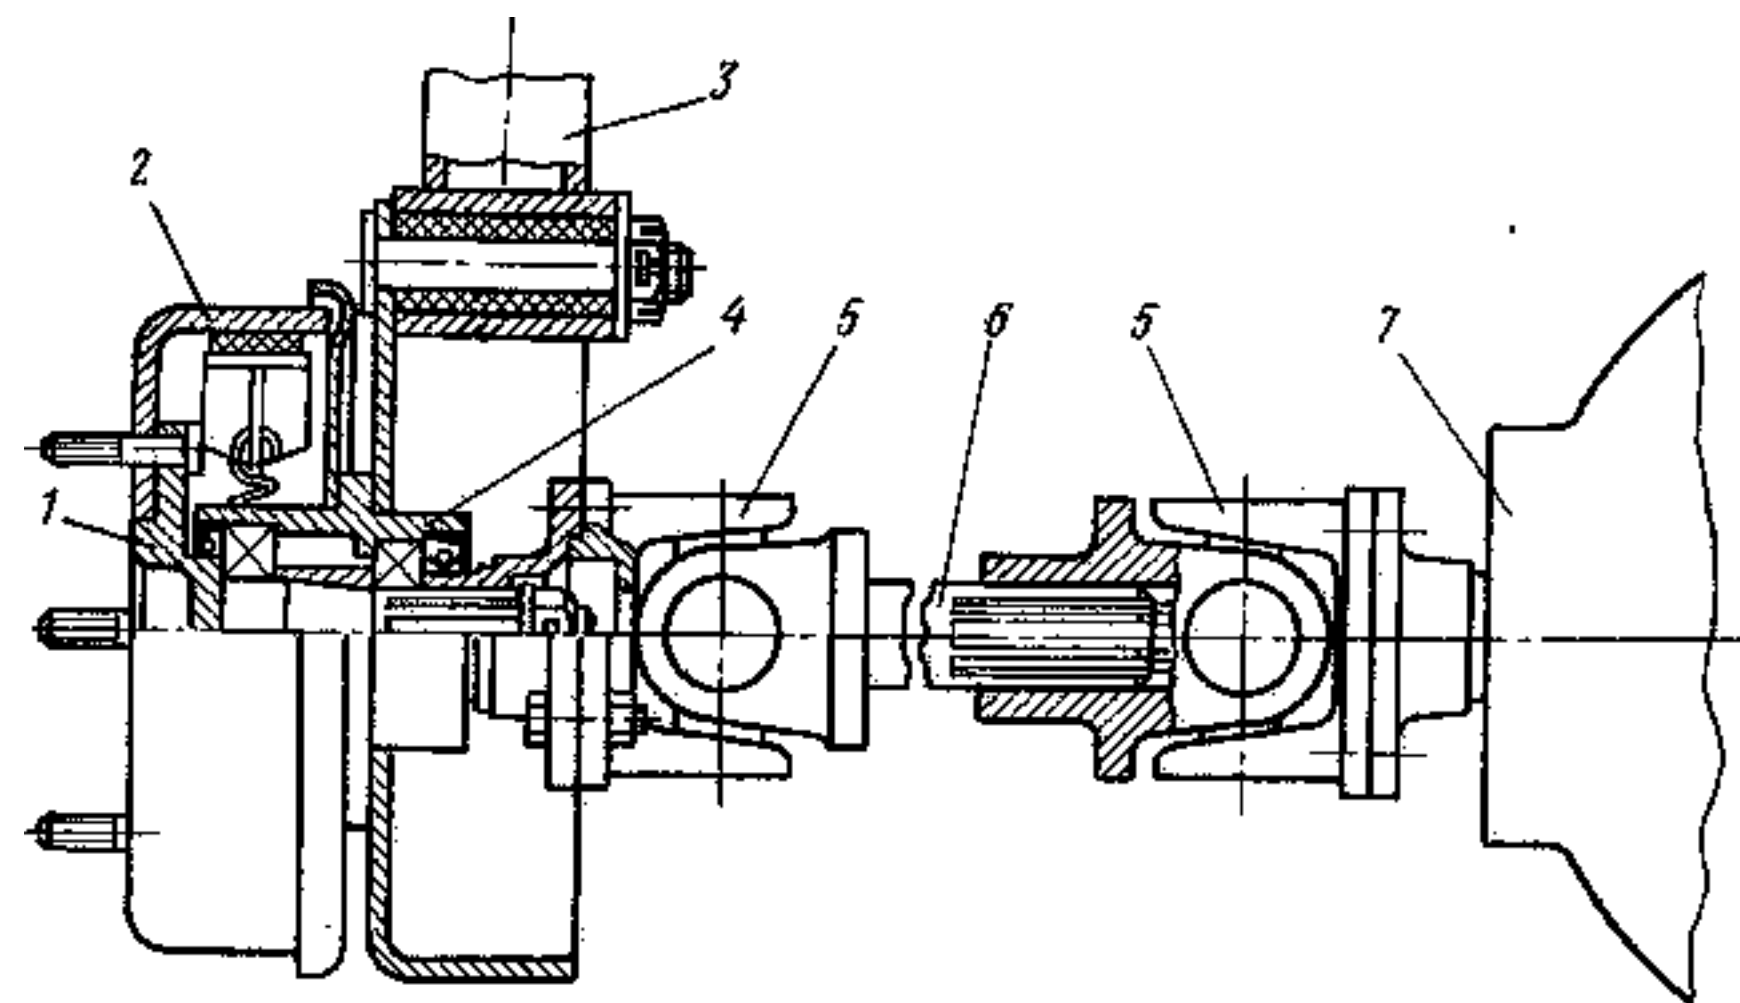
Привод ведущих колес автомобиля «Колобок»:
